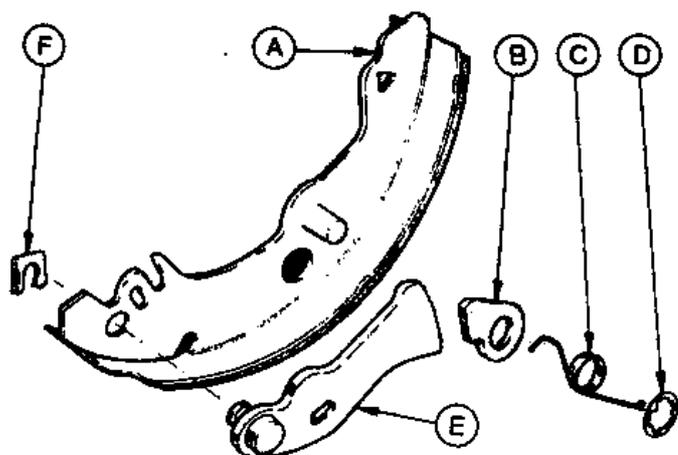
Передняя колодка (А), короткий рычаг храповика (В), пружина собачки (С), пружинная шайба (D), длинный рычаг храповика (Е) и клипс (F) (Разд.8)
